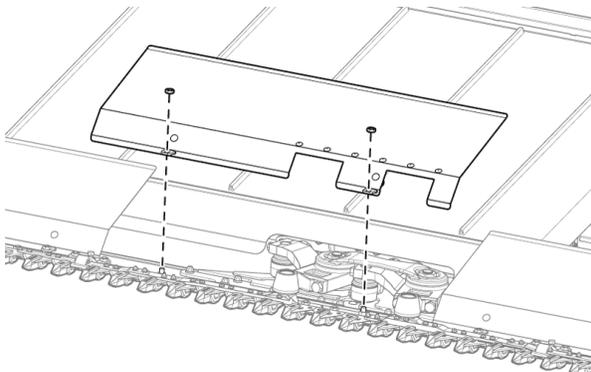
Снятие перьевой пластины, расположенной над подшипниками ножей.
